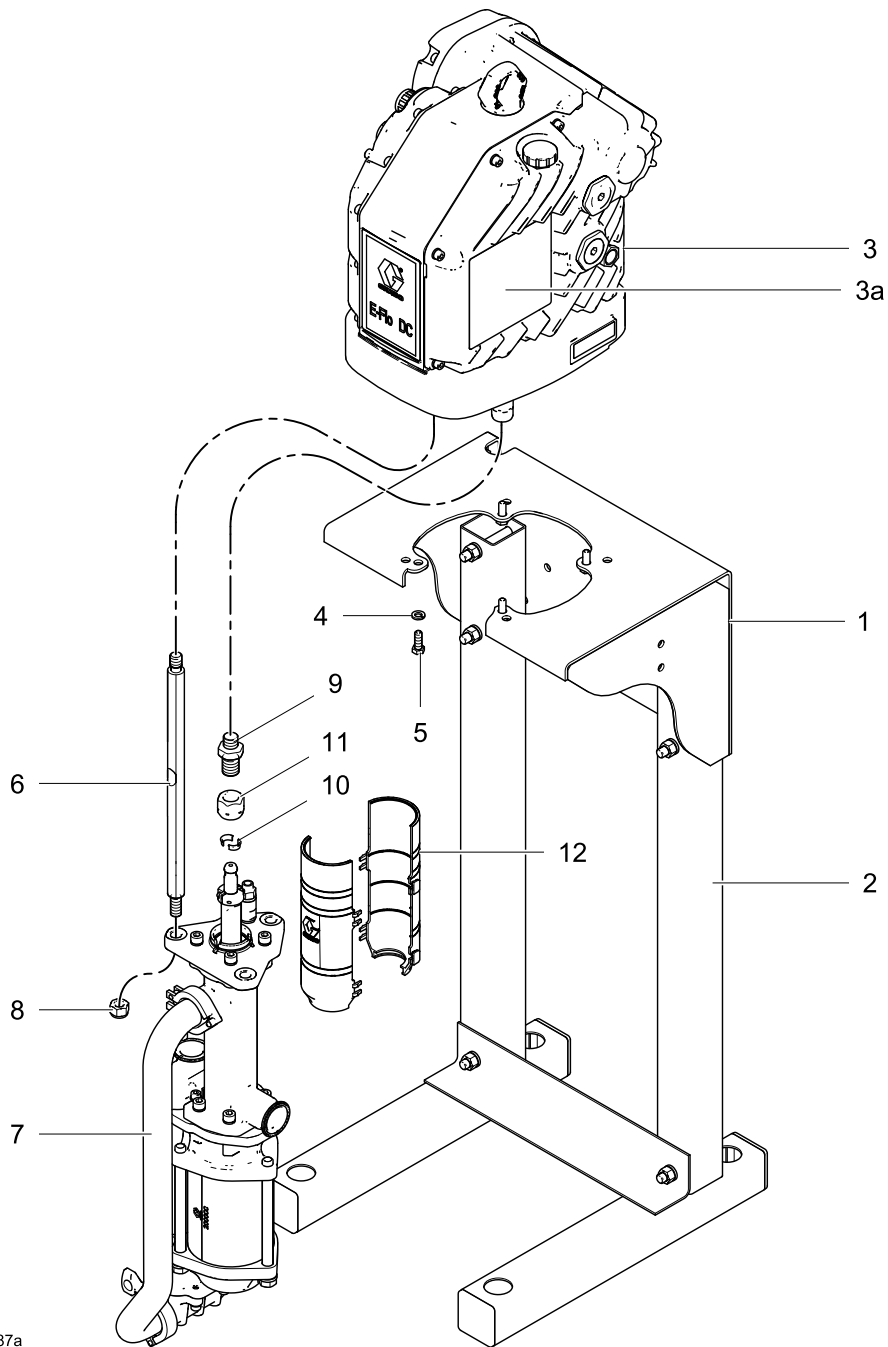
Pumpenmontage; Unterpumpe mit offener Ökertasse ist abgebildet
